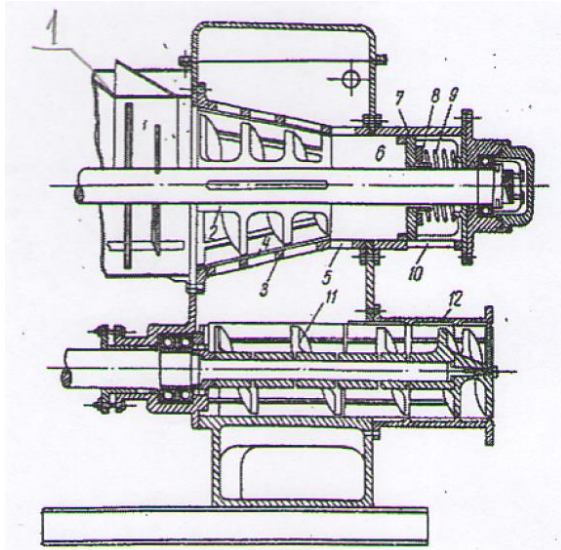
Вакуумный пресс с устройством камнеудаления: 1-Глиномешалка, 2-шnek, 3-решетчатый корпус, 4-сменные ребра, 5-отверстие, 6-камера каменистых включений, 7-поршень, 8-гайка, 9-пружина, 10-выгрузочное окно, 11-винтовые ножи, 12-головка пресса
